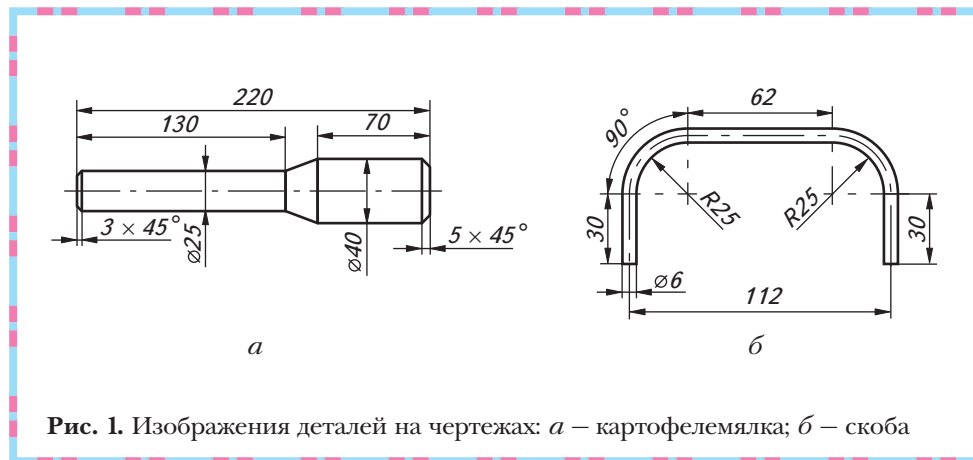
Изображения деталей на чертежах: а – картофелемялка; б – скоба
